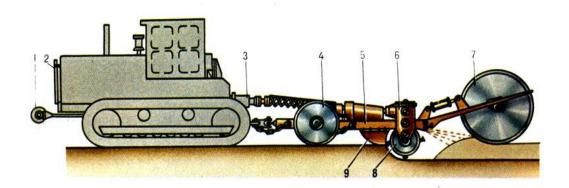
Схема кустореза МТП-42А: 1 - валочный брус, 2 - предохранительная решётка радиатора, 3 - карданный вал, 4 - передние колёса, 5 - рама, 6 - трансмиссия, 7 - опорный каток, 8 - фрезерный барабан, 9 - отбойная плита
